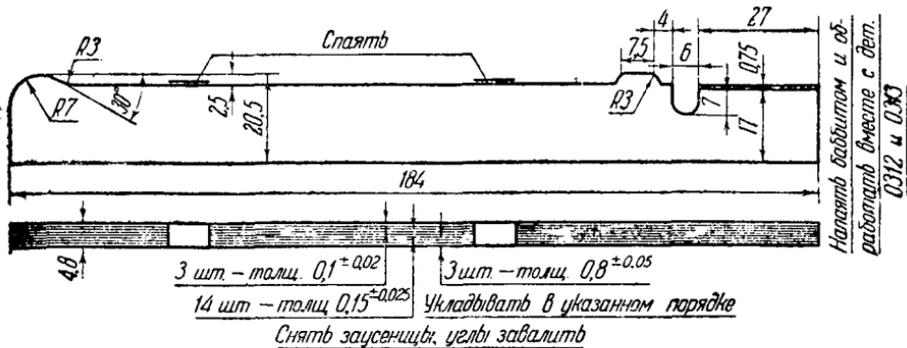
Дет. № 0315. Прокладка заднего коренного подшипника регулировочная
